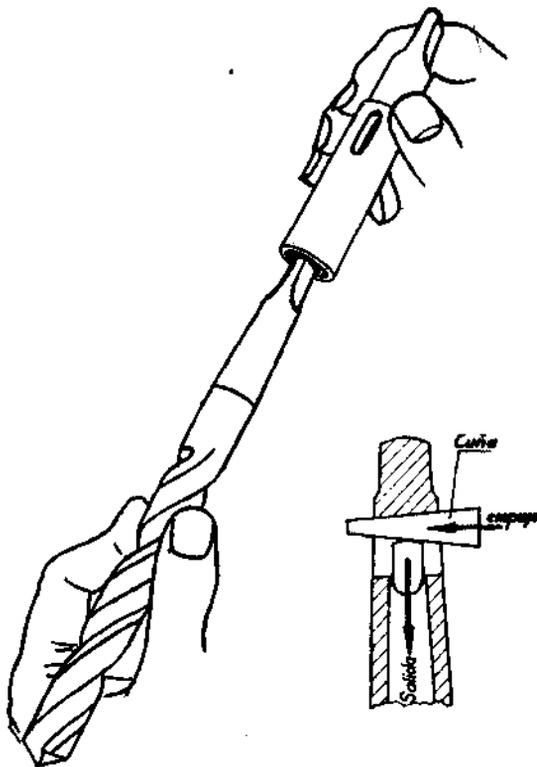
Montaje y desmontaje de un casquillo de acoplamiento
